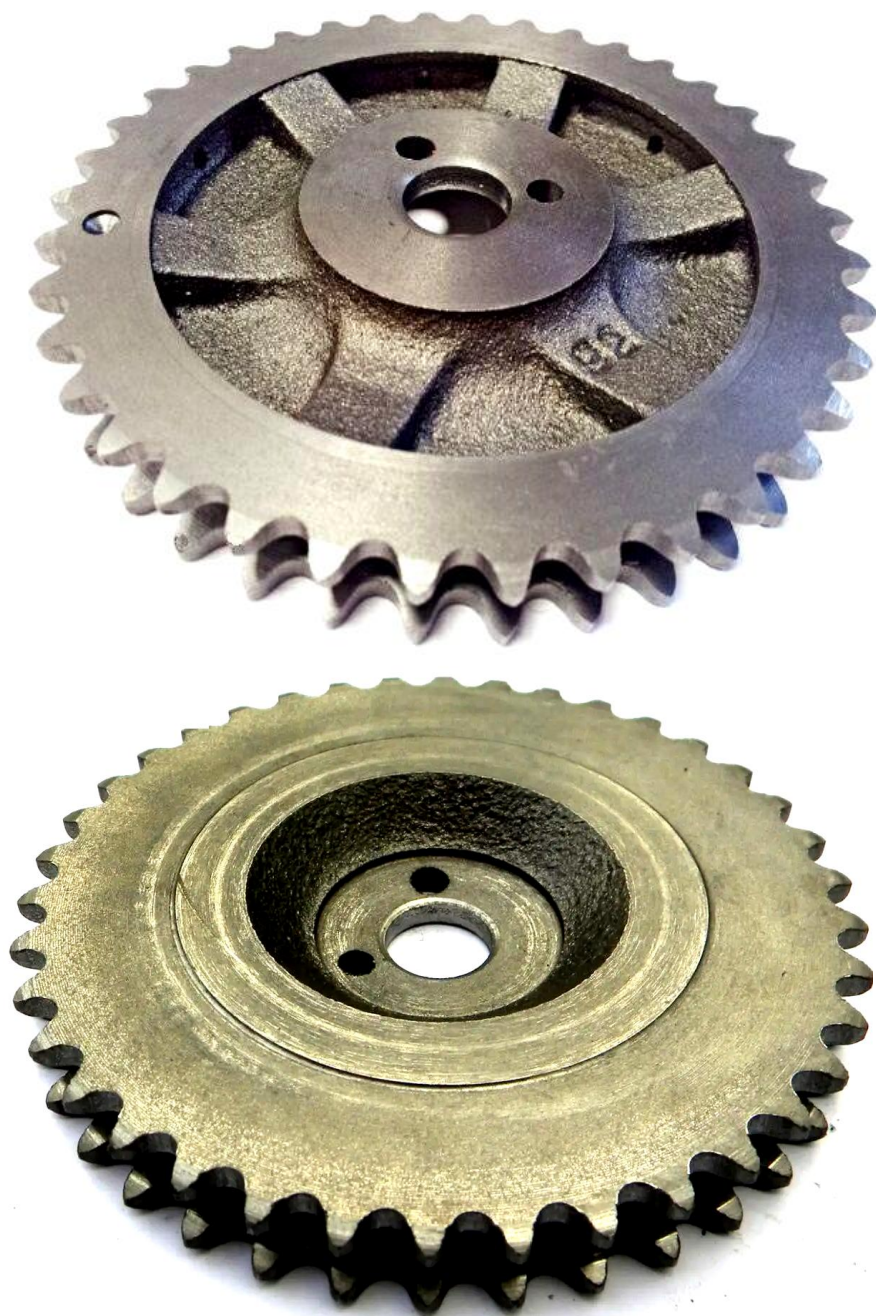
Зірочка приводу розподільного вала двигуна ВАЗ-2101
